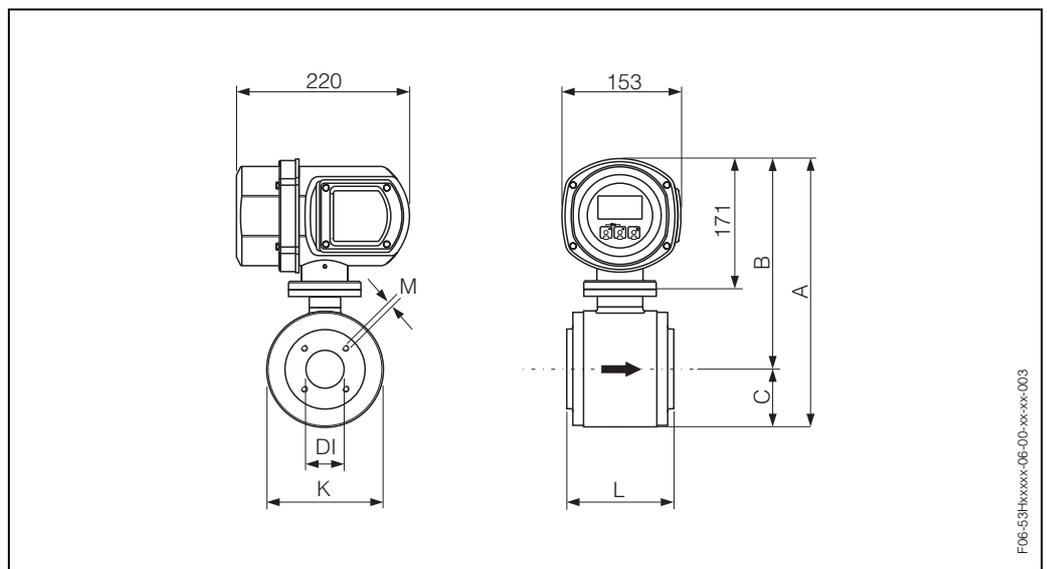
Abmessungen Promag H / DN 40... 100 (Kompaktausführung, Edelstahl-Feldgehäuse)
